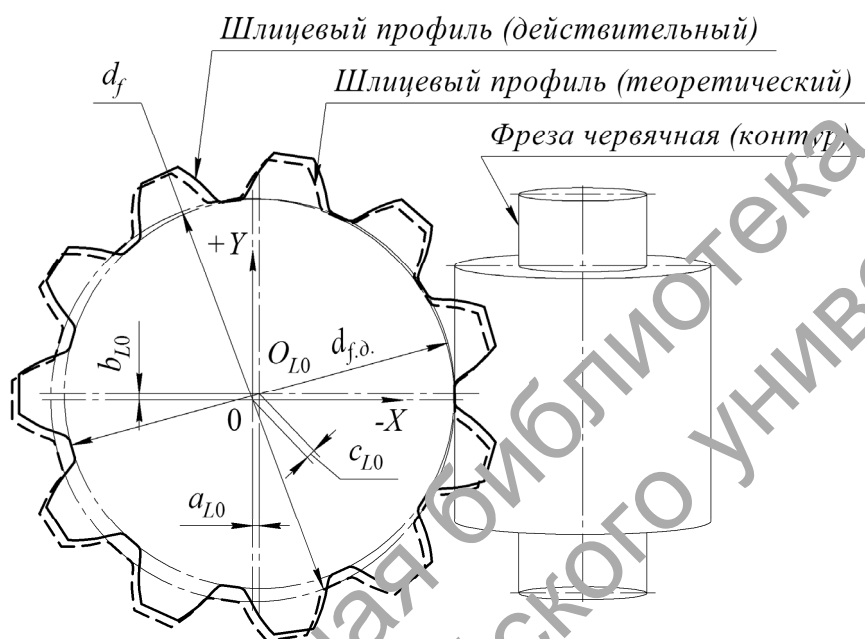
Схема взаимного расположения заготовки относительно фрезы
